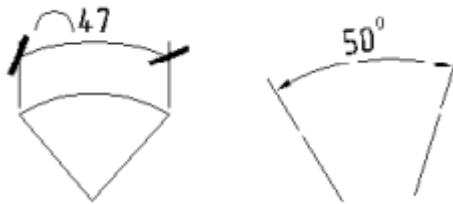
Нанесение: а – длины дуги; б – размера угла
